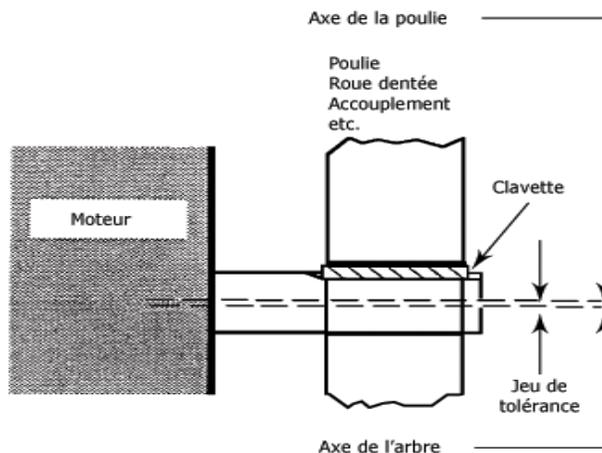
RATTRAPAGE DU JEU DE TOLERANCE. [58]
